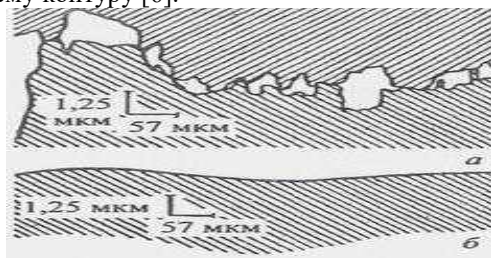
Профиль поверхности: а - двух собранных медных деталей перед ультразвуковой сваркой; б - нижней детали после воздействия ультразвука [10].
